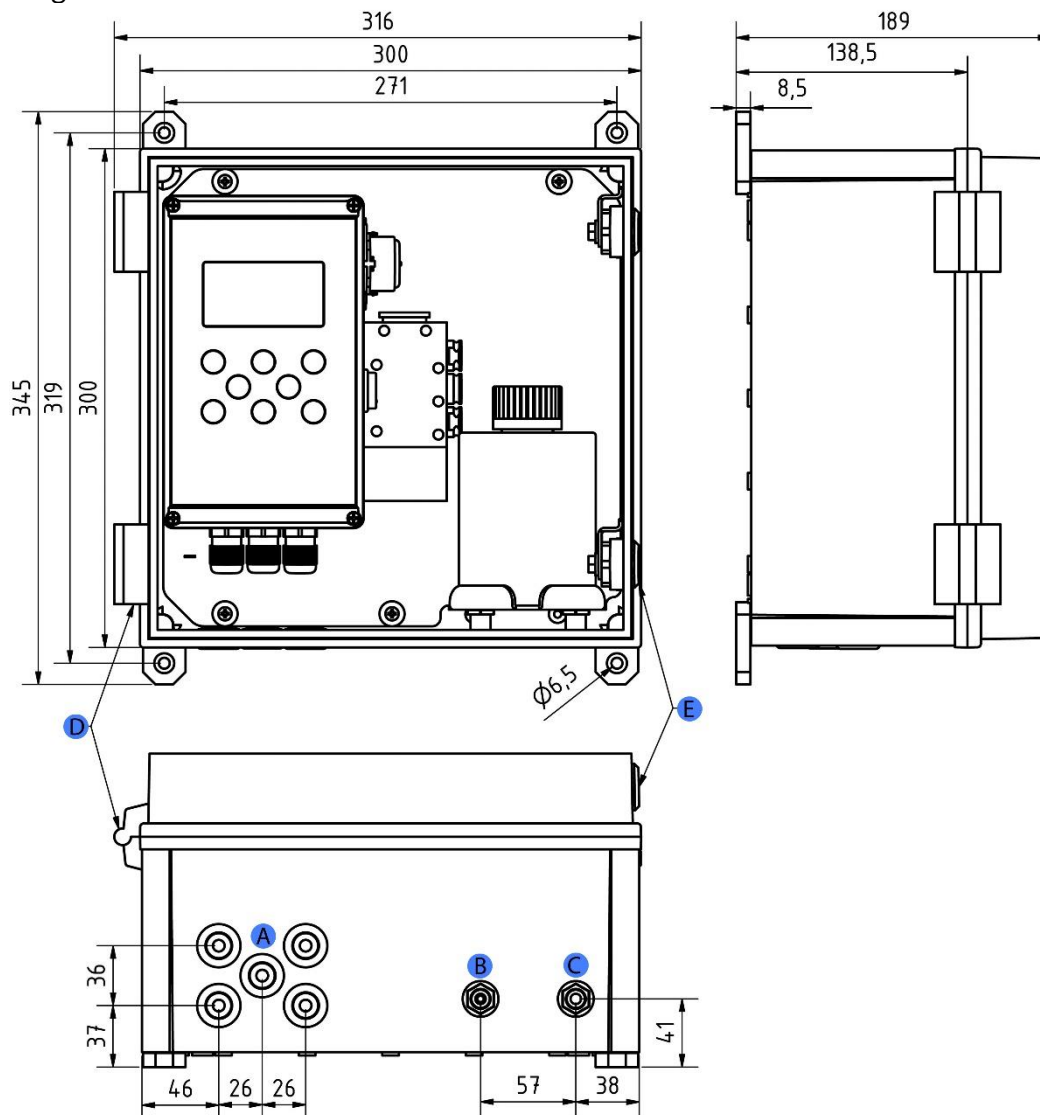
Bohrplan zur Befestigung des Analysegerätes im Gehäuse
